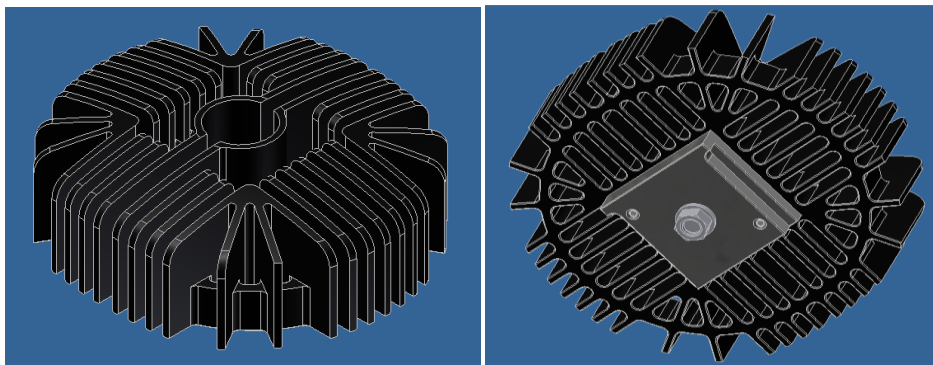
Upnutí inovovaného přípravku do upínací desky
